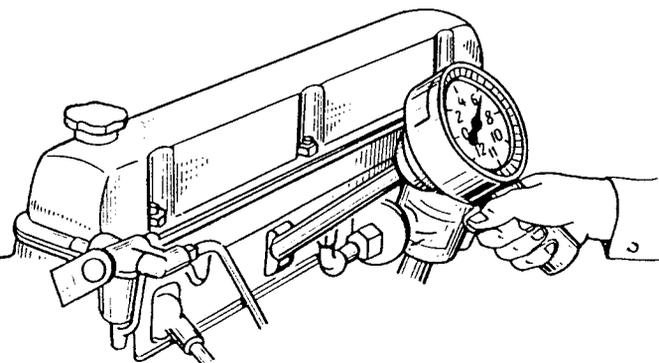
Prüfung der Verdichtung in den Motorzy-lindern
